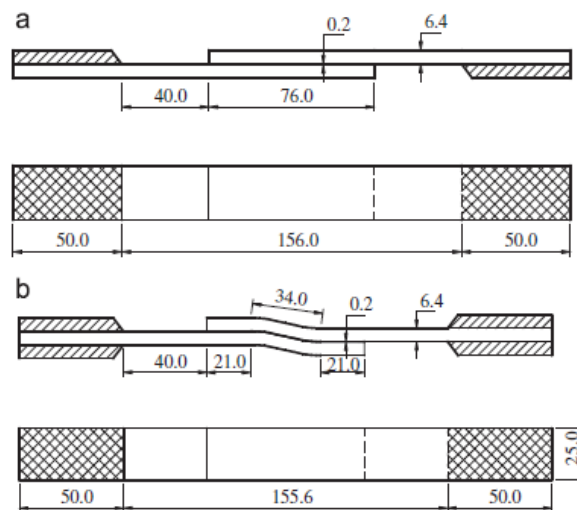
Geometria de uma junta adesiva: a) Junta de sobreposição simples; b) Junta ondulada [123]
